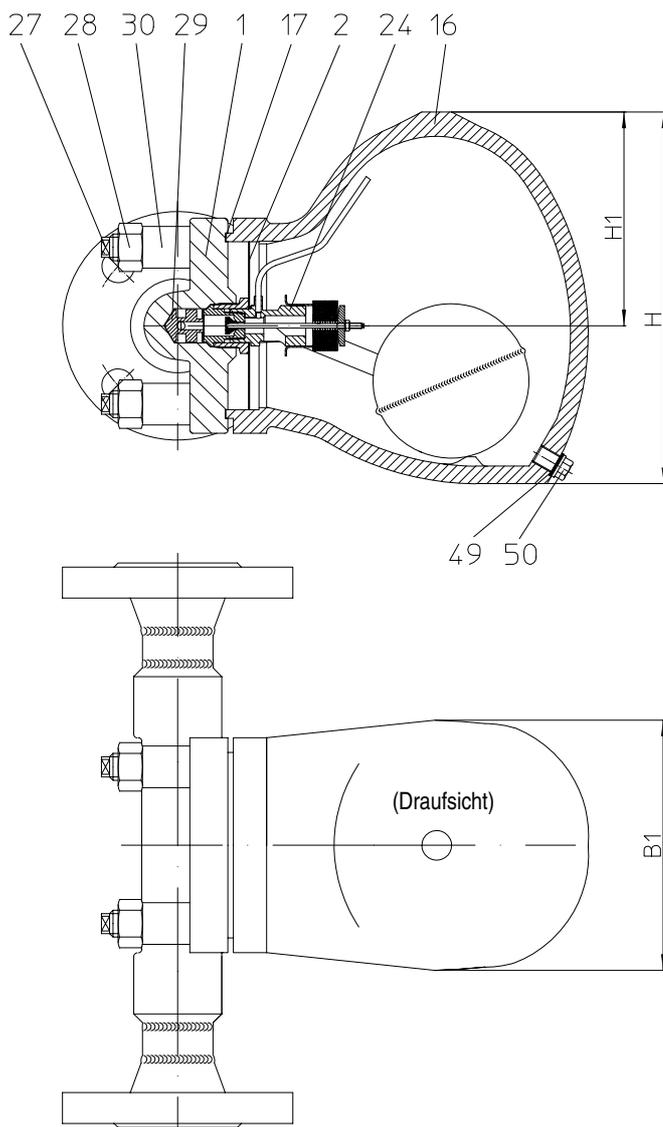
1 mit Flanschen - horizontale Einbaulage (PN100)
